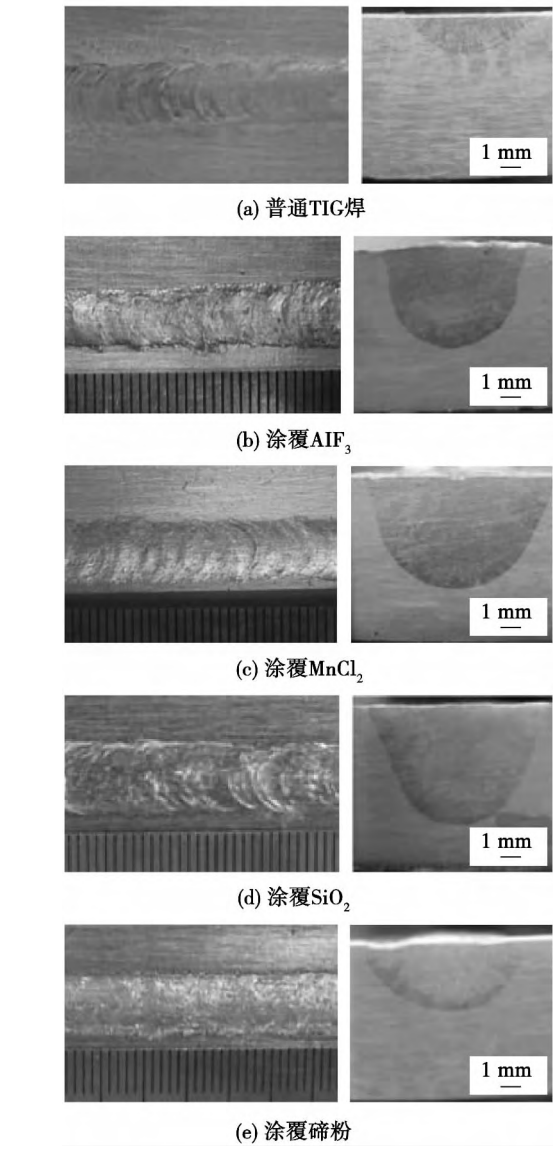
TIG 焊和 GTFA-TIG 焊的焊缝形貌
